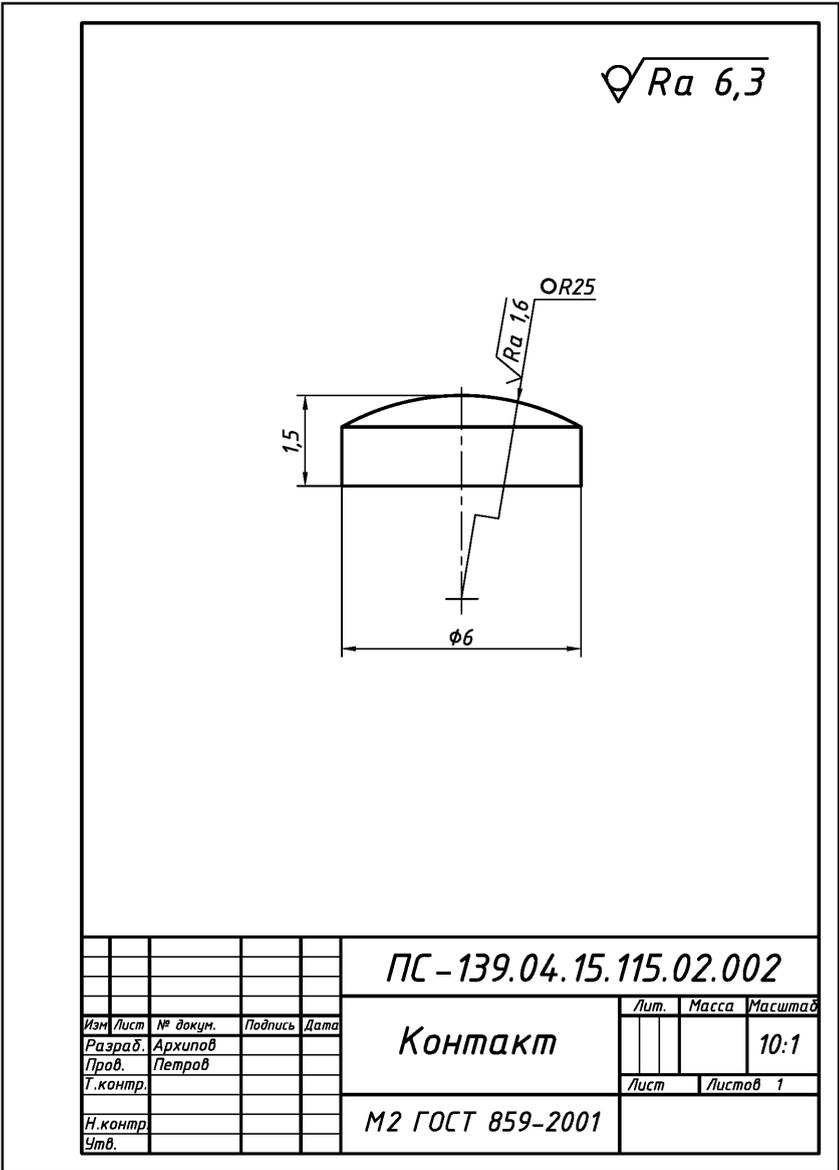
Оформление рабочего чертежа детали «Контакт»
